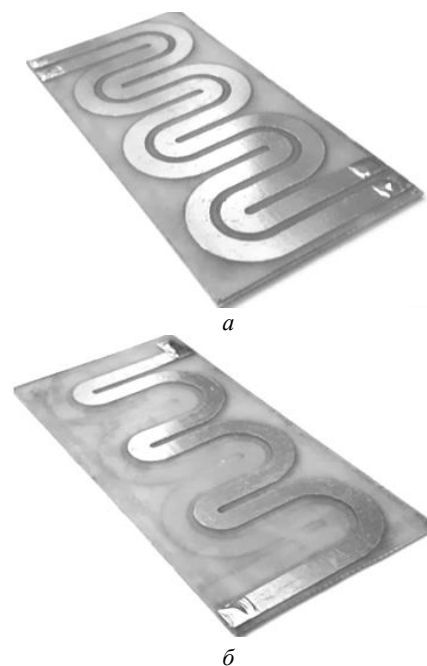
Изготовленный макет: вид сверху (а) и снизу (б)
